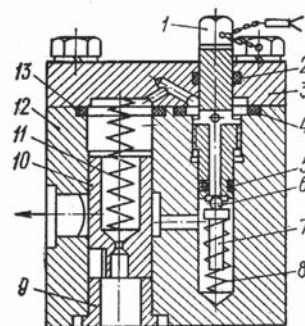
Запобіжний клапан непрямої дії: 1 — шпіндель; 2, 4, 5, 13 — гумові ущільнювальні кільця; 3 — кришка; 6 — кулька; 7 — шток; 8, 11 — пружини; 9 — втулка; 10 — поршень; 12 — корпус.
